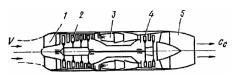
Схема ТРД: I — входное устройство (воздухозаборник); 2 — компрессор; 3 — камера сгорания; 4 — газовая турбина; 5 — выходное устройство (реактивное сопло)
